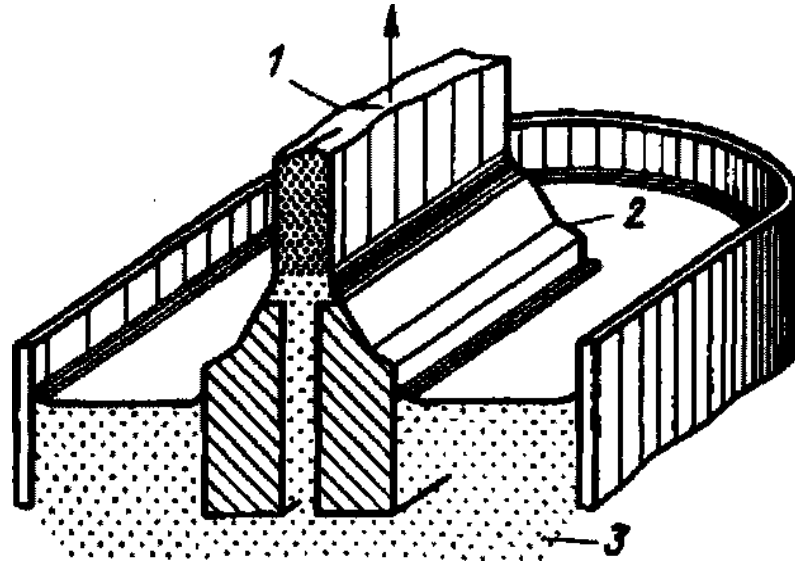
Спрощена схема вирощування кремнієвої стрічки EFG-способом: 1 – кремнієва стрічка; 2 – формоутворювач; 3 – рідкий кремній
